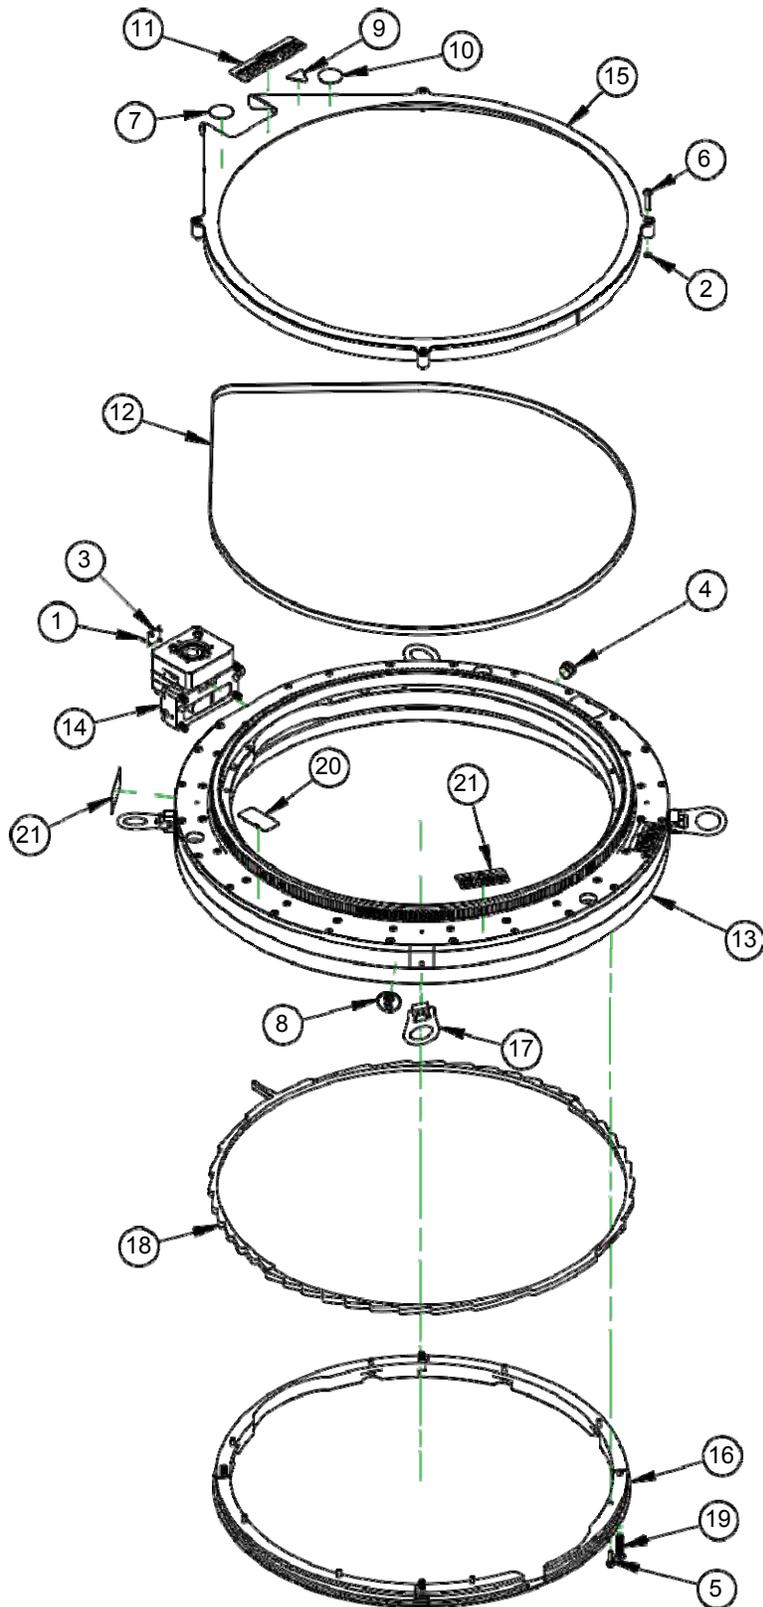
ENSEMBLE DE L'UNITÉ DE COMMANDE ROTATIVE DE LA FF2400 (RÉF. 79903)
